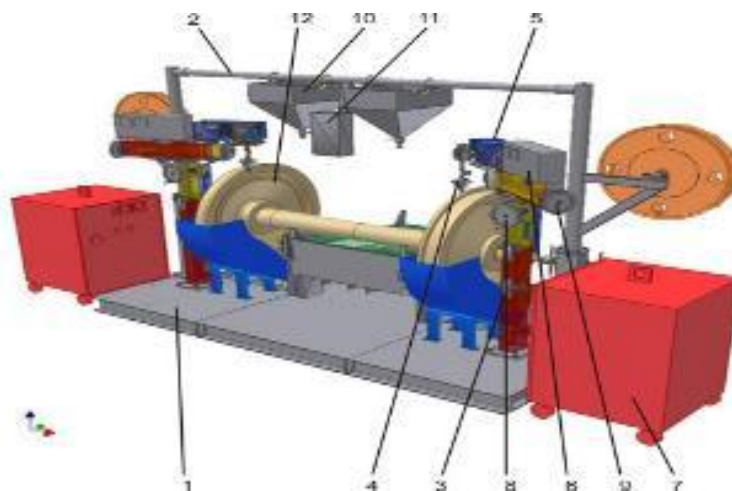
Установка для наплавки гребней железнодорожных колёс
